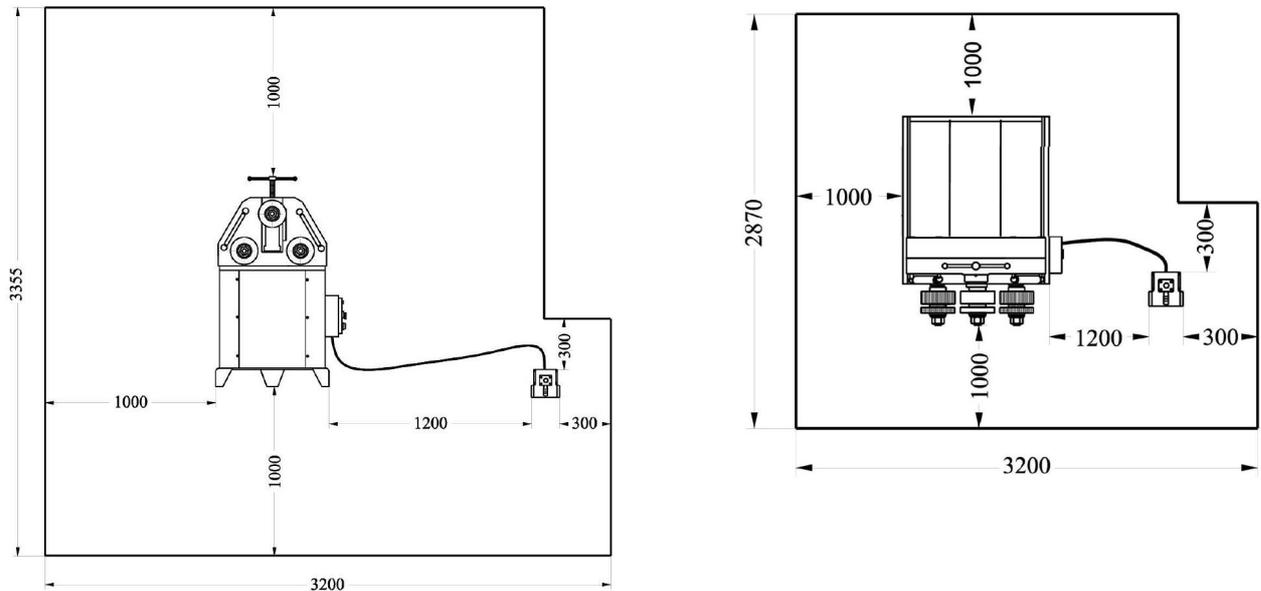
Platzbedarf der Ringbiegemaschine PRM 35 F - links vertikaler Betrieb, rechts horizontaler Betrieb
